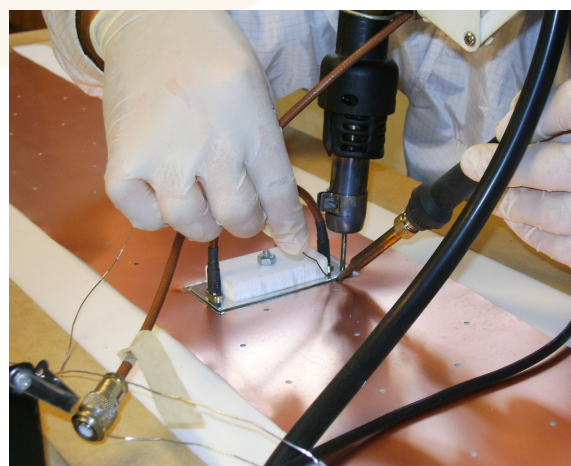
Soldando la parte de atrás de un módulo radiante.
